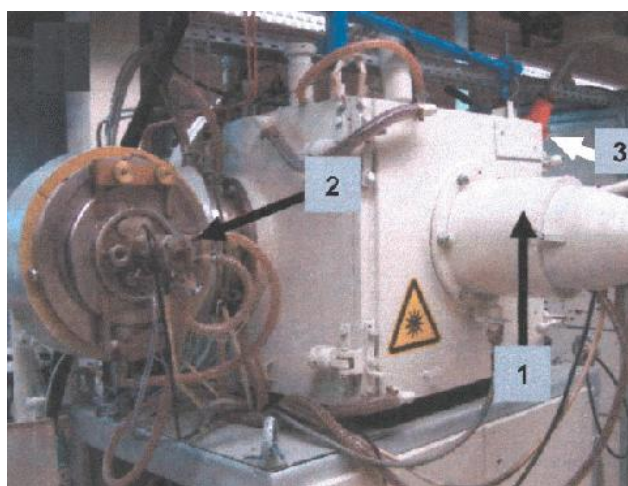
Установка «Кремень-Д». Общий вид
